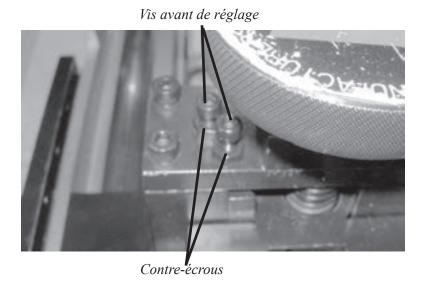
Vis avant de réglage du serrage du porte-outil mâle.
